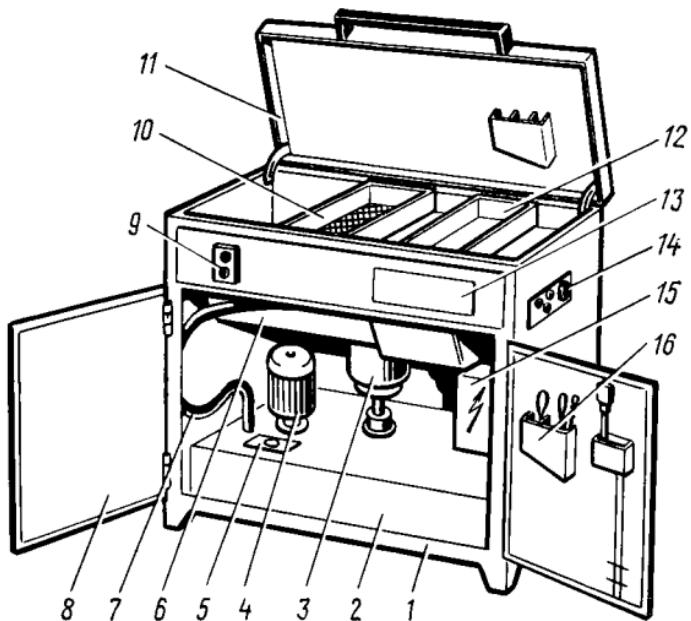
Установка ОРГ-4990Б-ГОСНИТИ:
